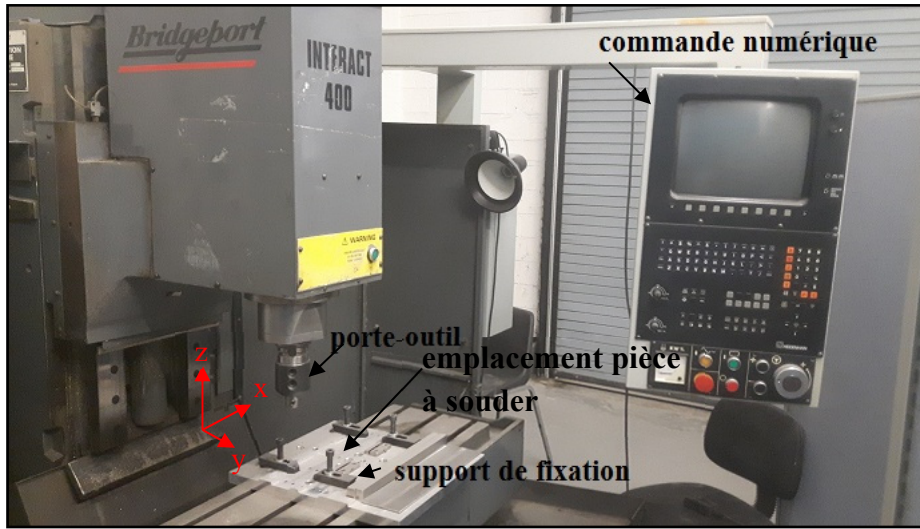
Machine de soudage par friction-malaxage de l'ÉTS
